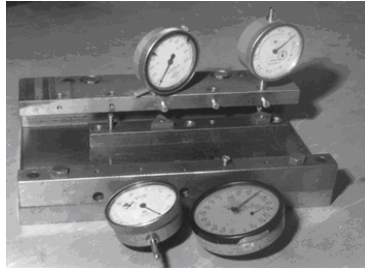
Приспособление для измерения высоты h в вершинах пластин
